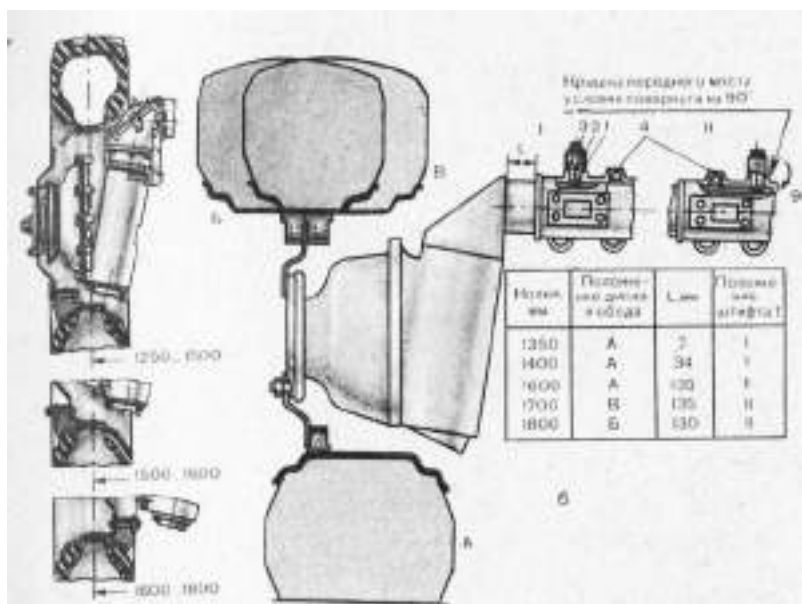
Схемы расстановки передних ведущих колес тракторов: а — МТЗ-82; б — МТЗ-102; 1 — штифт; 2 — стакан; 3 — болт; 4 — заглушки; 1 и 11 — различные положения штифта 1; А, Б и В — положения диска и обода.
